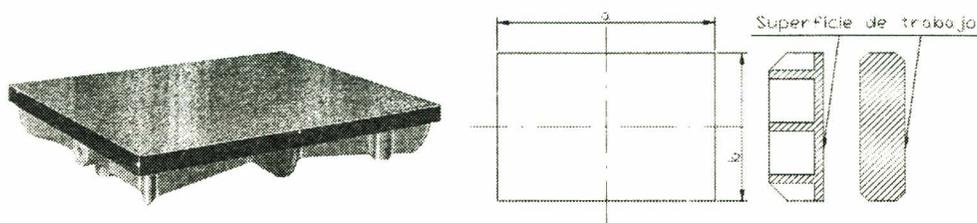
Mesa de planitud de fundición, (Mitutoyo) y vistas.
